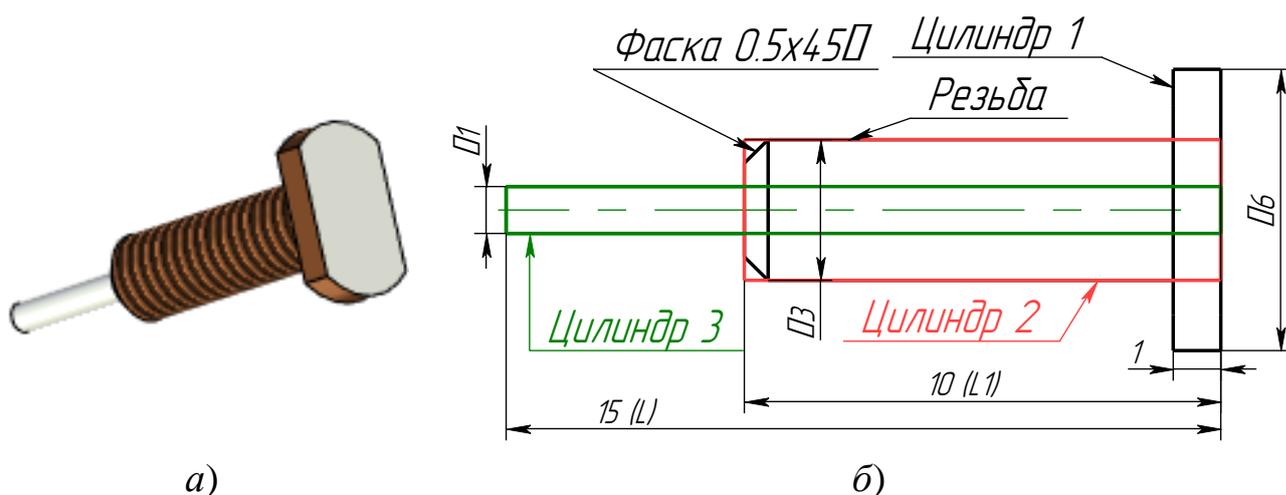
Контакт: а – внешний вид; б – размеры
